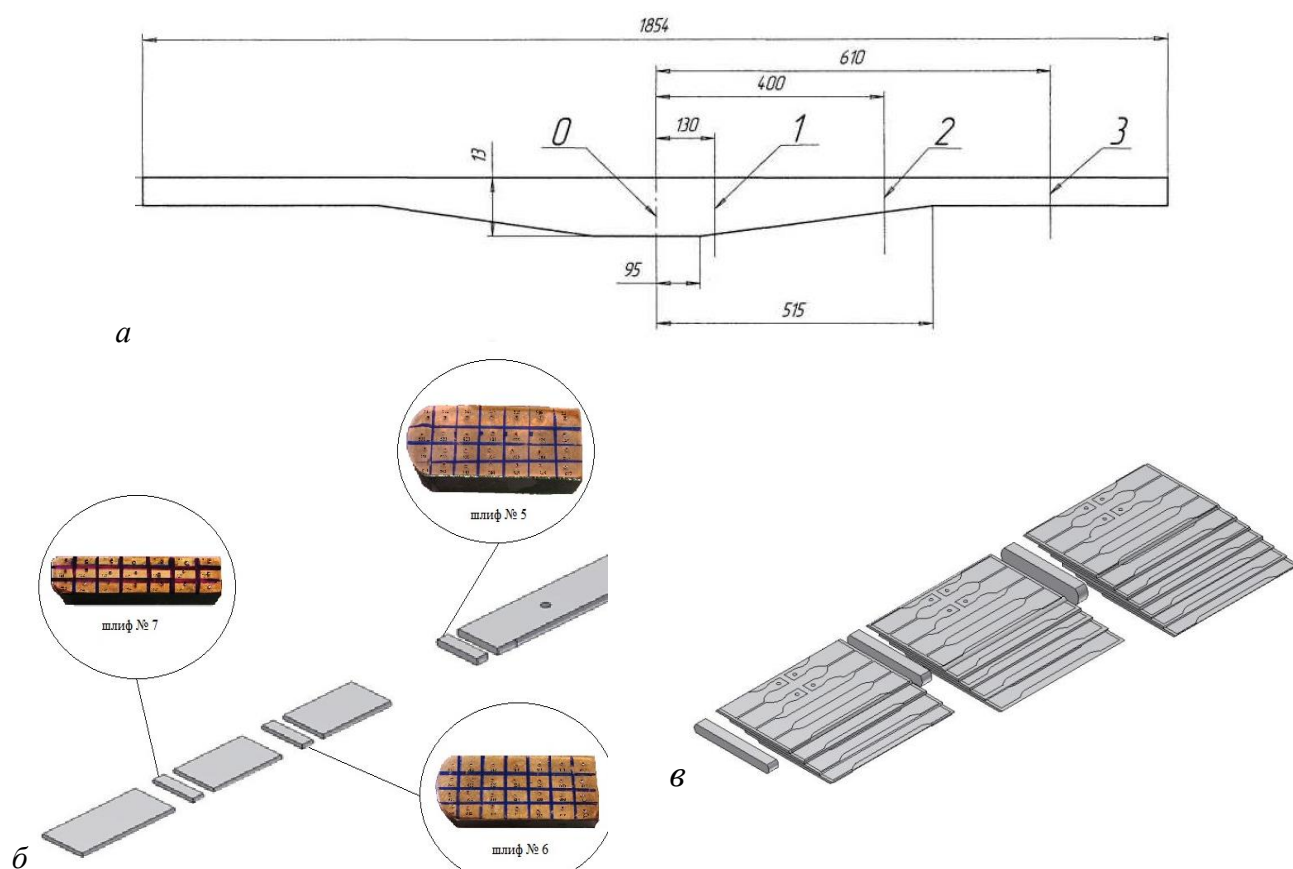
Эскиз прокатанной заготовки с клиновым профилем (а); схема резки участков заготовки со степенями обжатия: 1 - 4%, 2 - 23%, 3 - 40% - на зоны (б) и пластины (в)
